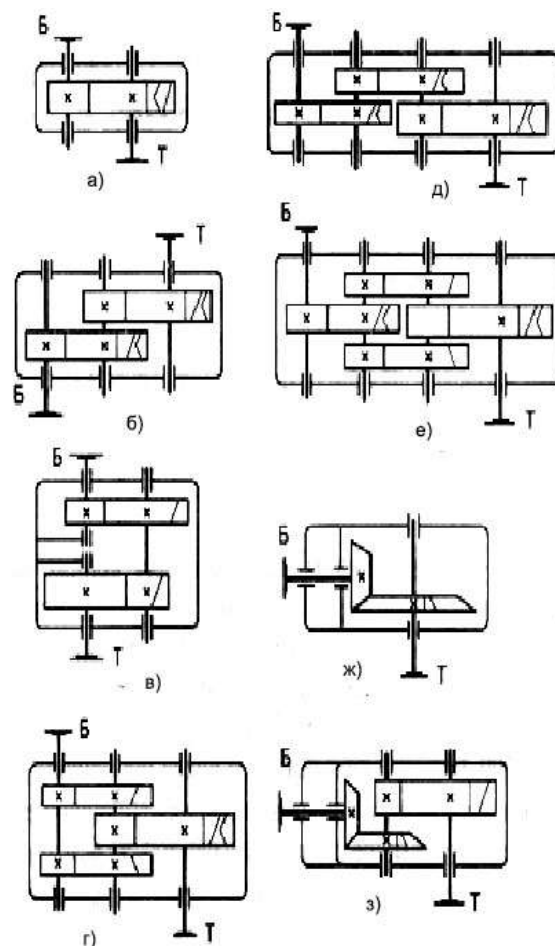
Наиболее распространенные схемы зубчатых редукторов: а — одноступенчатый; б — двухступенчатый развернутый; в — двухступенчатый соосный; г — двухступенчатый с раздвоенной ступенью; д — трехступенчатый развернутый; е — трехступенчатый с раздвоенной промежуточной ступенью; ж — конический; з — коническо-цилиндрический
